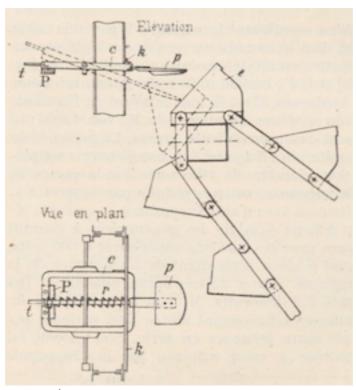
et 4. — Élévation et plan de la pelle à débourrer, système Delvaux.
